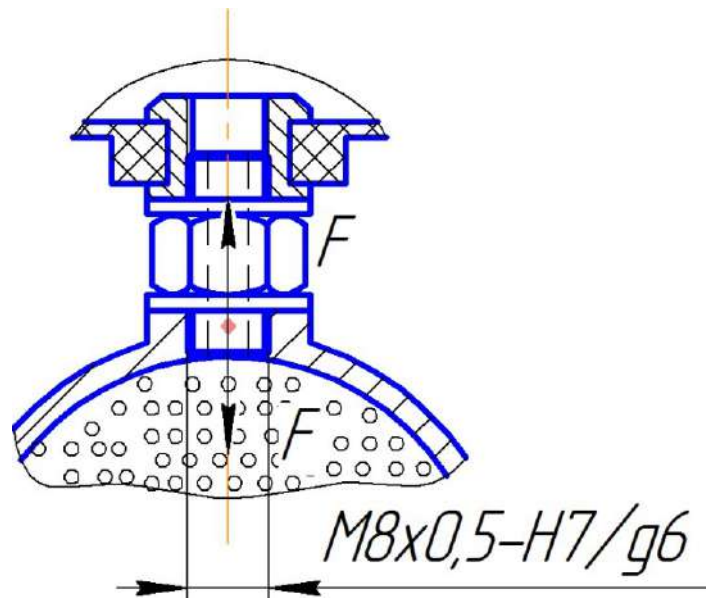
Розрахункова схема різьбового з'єднання Зусилля затягування різьбового з'єднання дорівнює:
